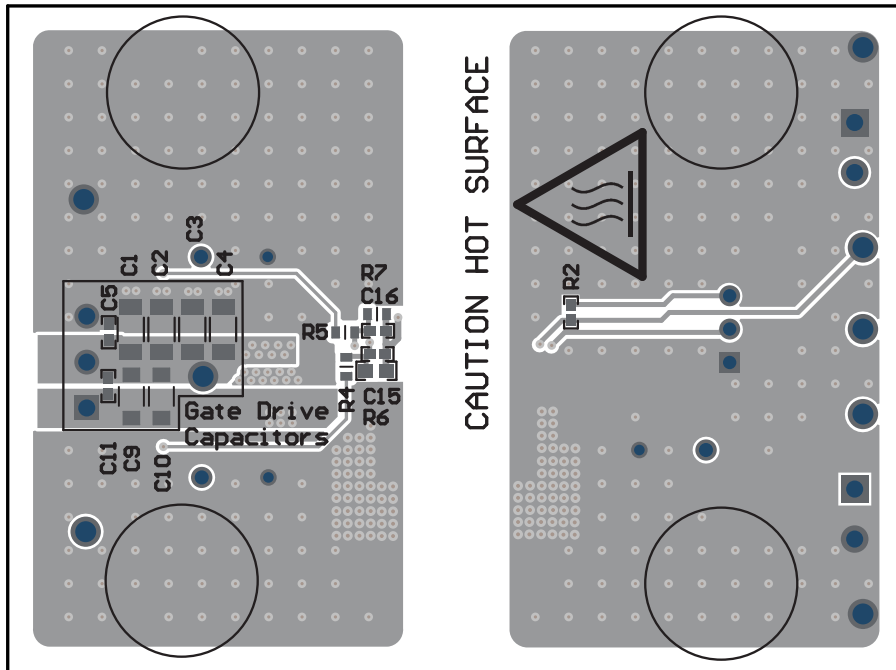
UCC14341EVM-069 , PCB 底层 , 组装 (镜像视图)
